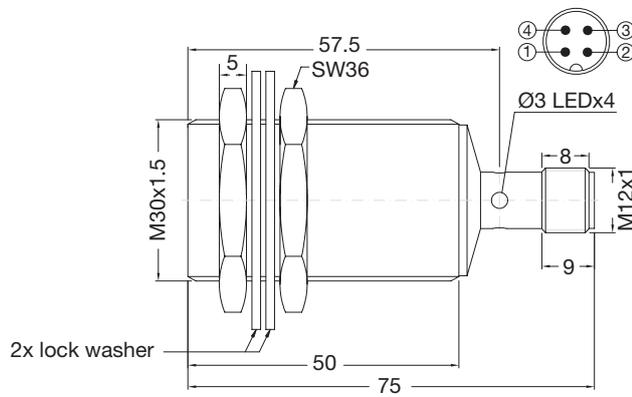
Lange Ausführung, bündiger Einbau, Steckversion
